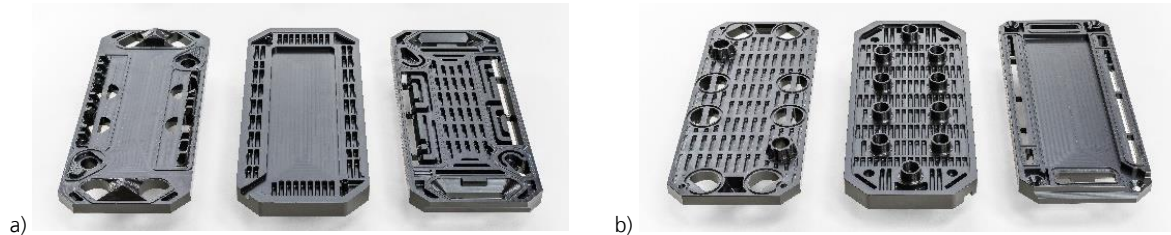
Frästechnisch hergestellte Prototypen der IDM-Platten (Flach)
